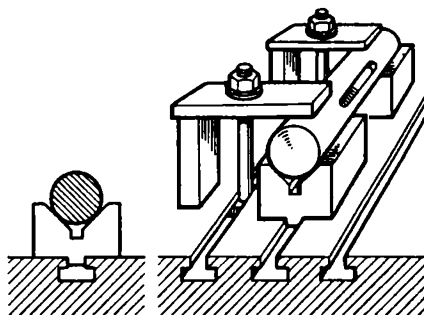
Закрепление цилиндрической заготовки в призме
